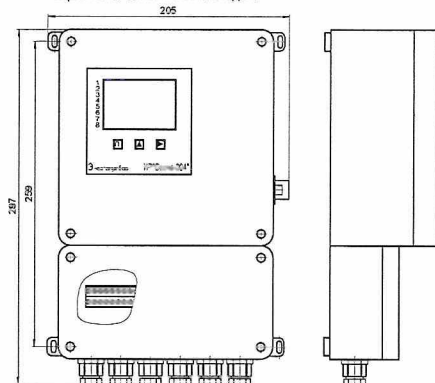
Габаритные и установочные размеры ИР "Сосна-003"
